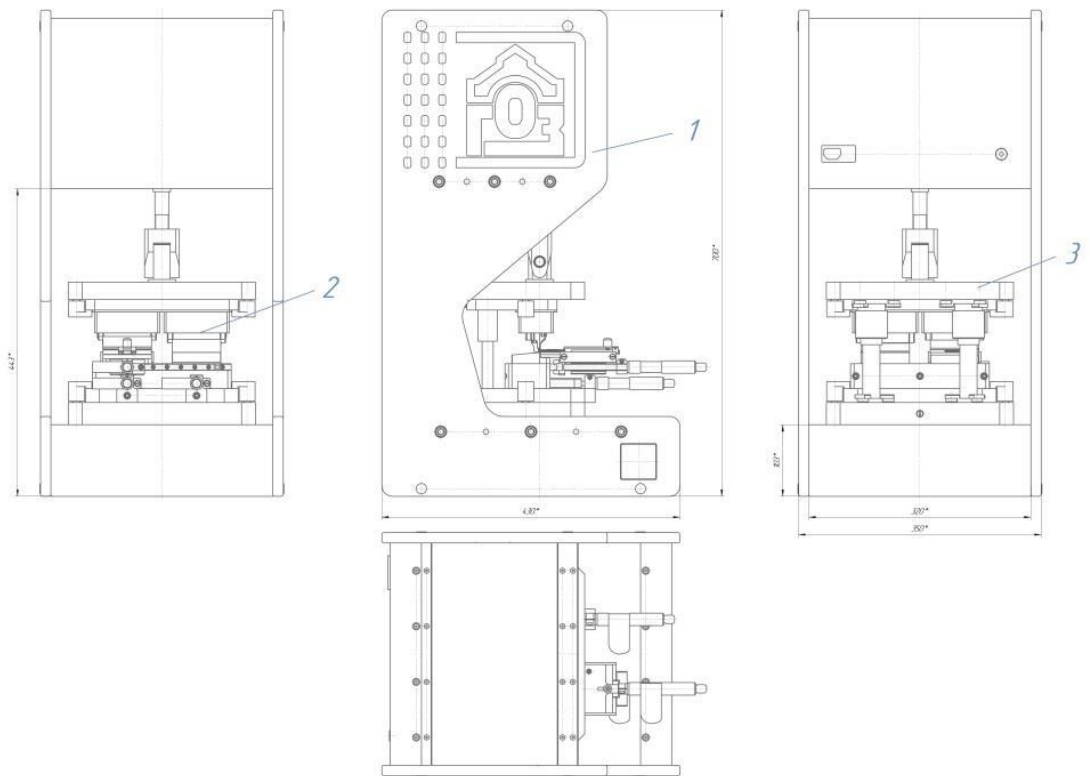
Пресс для формовки и обрезки выводов микросхем
